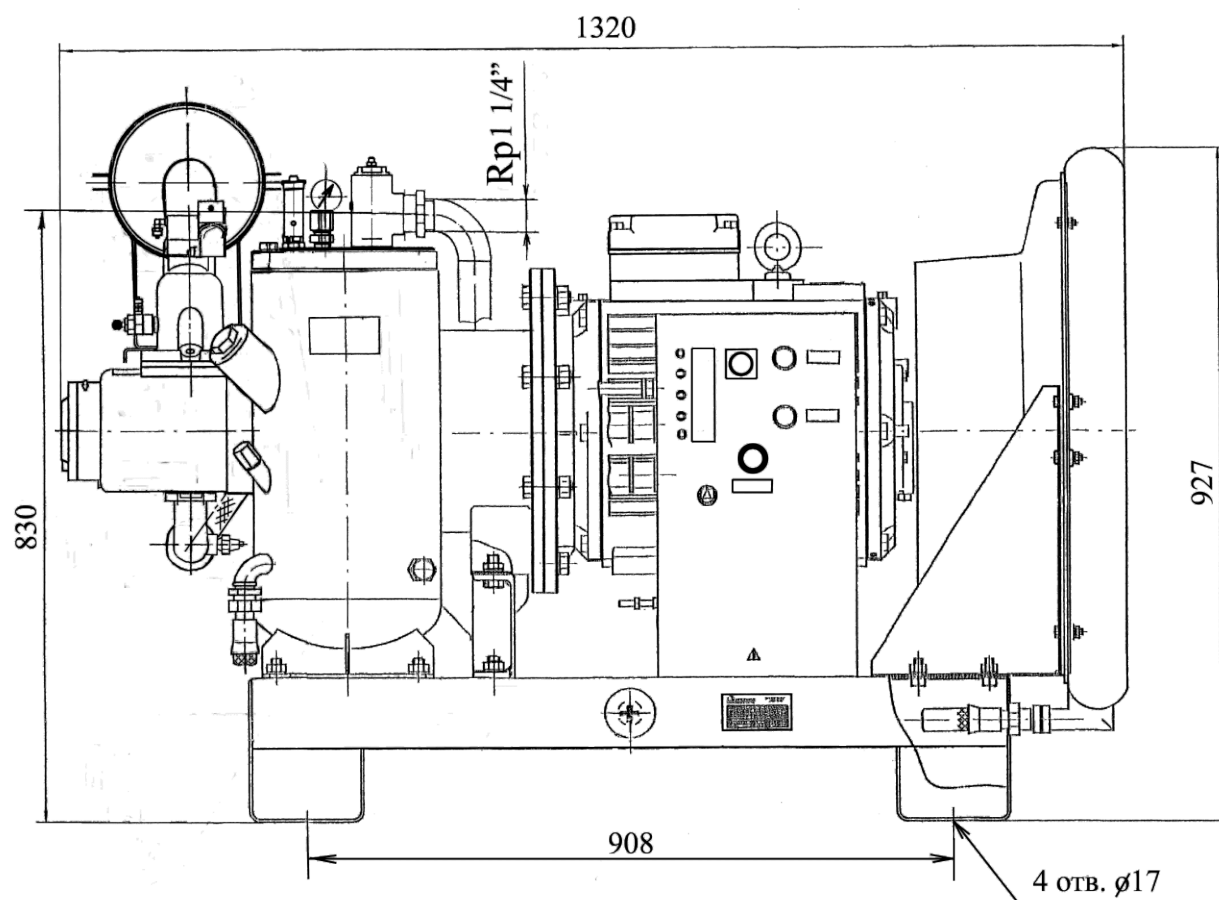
Габаритный чертеж станции компрессорной ЗИФ-СВЭЗ/0,7 (АРМ19-22)
